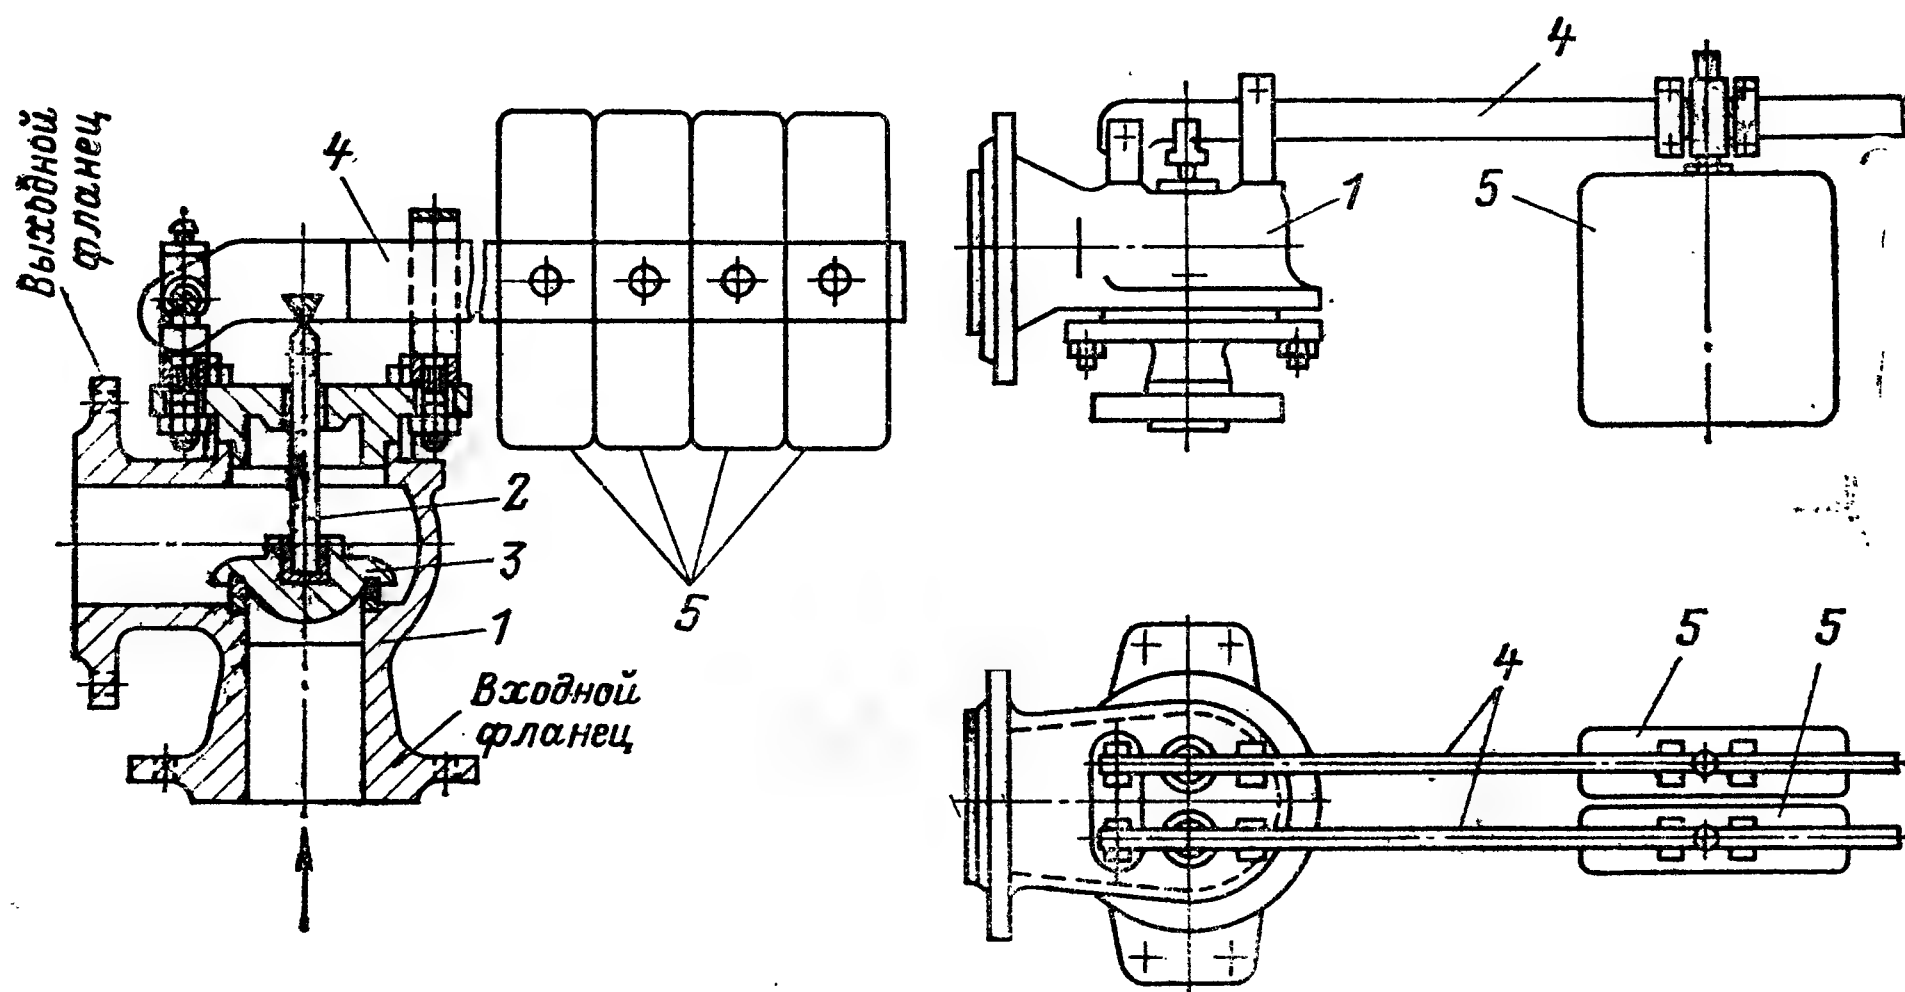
Рычажный предохранительный клапан с грузом.
